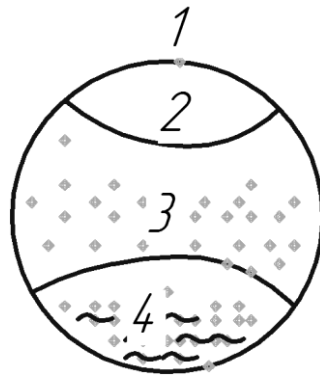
Поверхня втомного зламу деталі циліндричної форми [71]
